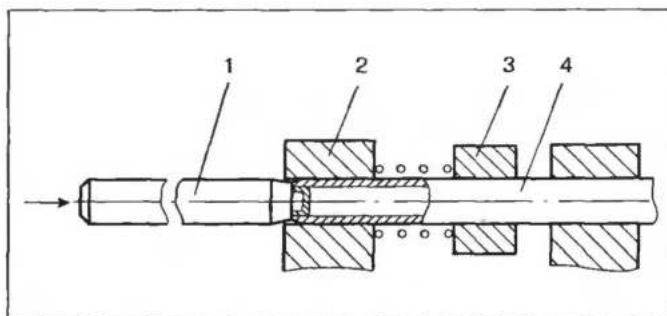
Схема выпрессовки оси коромысла: 1 — стержень из "мягкого" металла; 2 — головка блока; 3 — коромысло; 4 — ось
